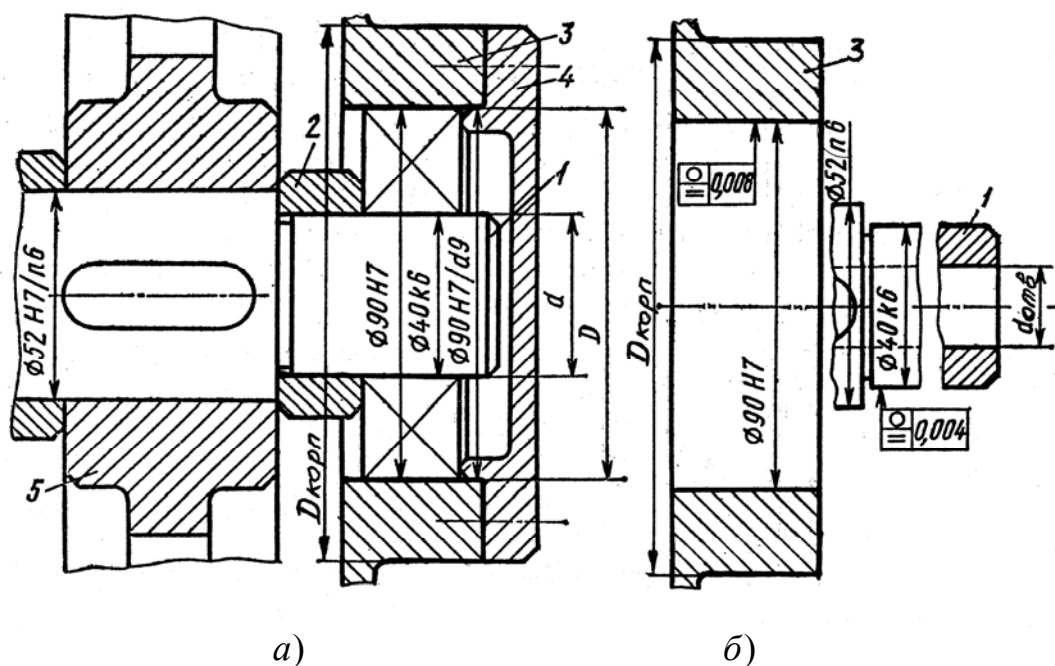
Обозначение посадок подшипников качения на сборочных чертежах (а) и полей допусков на чертежах деталей (б):
